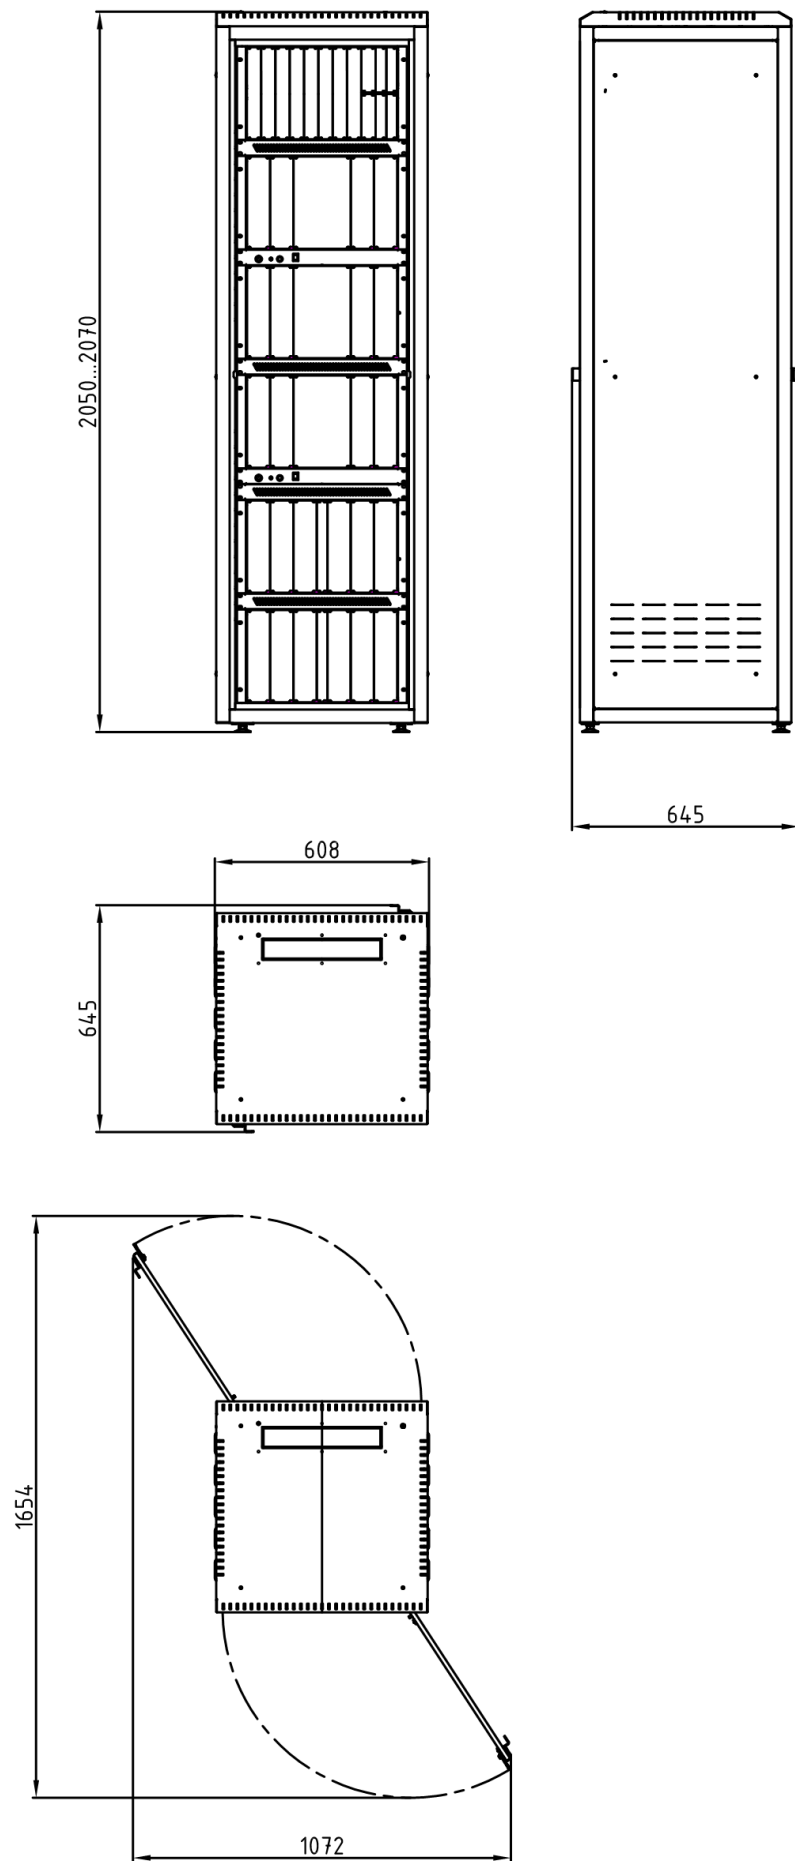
Габаритно-установочные размеры шкафа ЦМ КРЦ и первой ступени защиты исполнения 1
